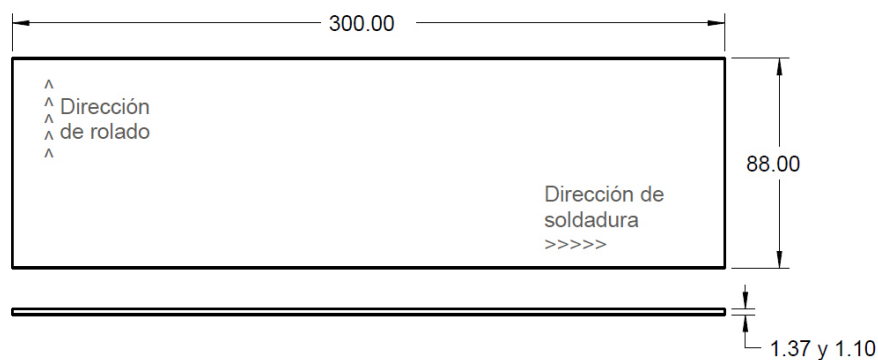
Cupones de soldadura utilizados para los dos aceros (dimensiones en milímetros).
